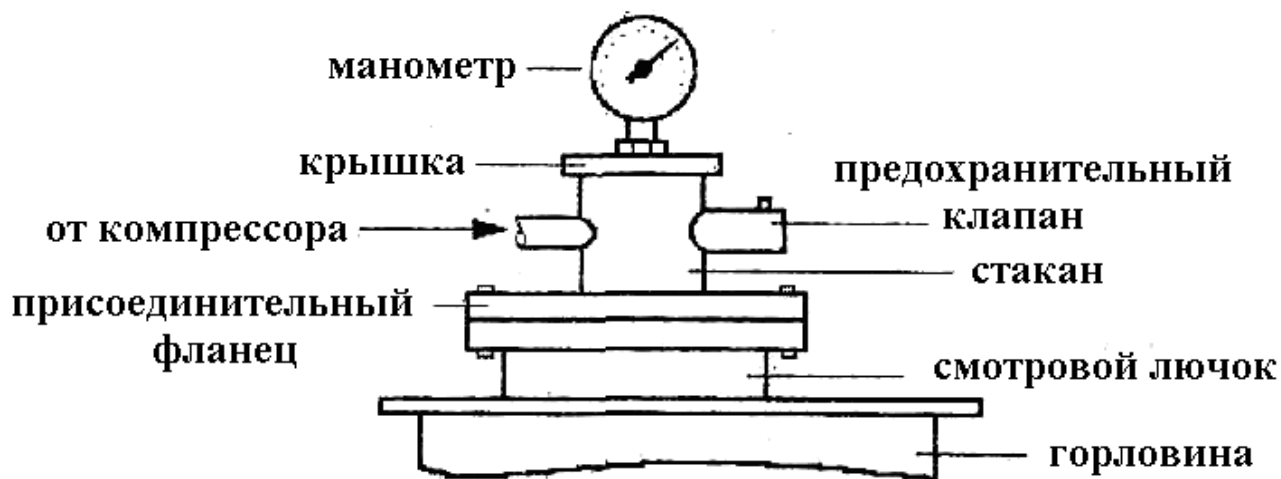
Приспособление для пневматической опрессовки резервуаров и цистерн.
